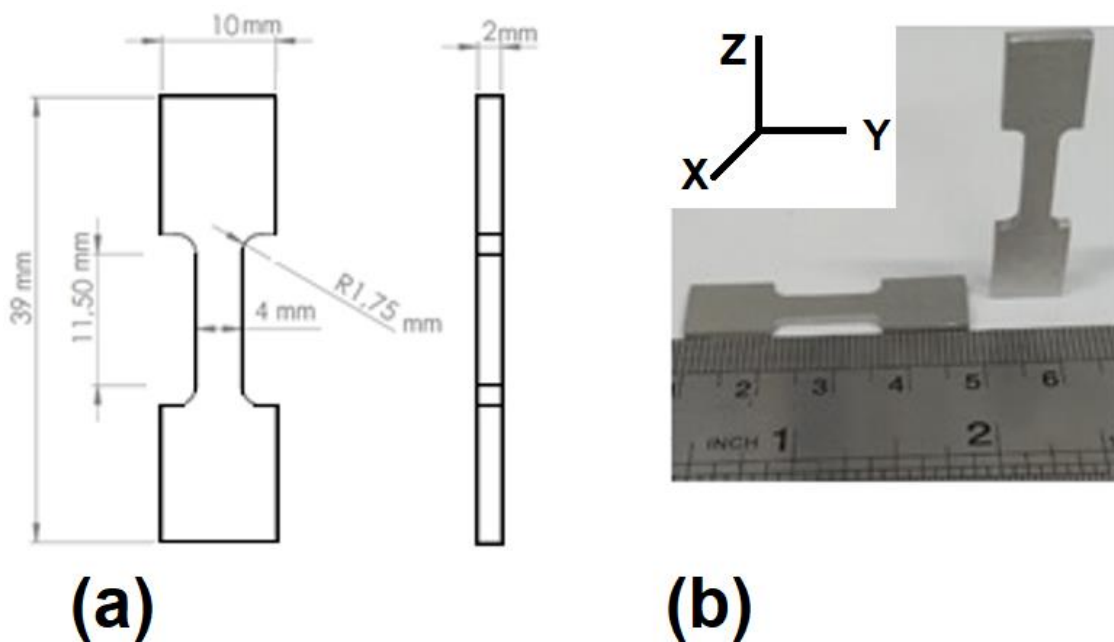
Corpo de Prova para ensaio de tração: (a) corpo de prova com dimensões reduzidas; (b) corpos de prova após usinagem com indicação dos planos em que as barras foram construídas por FSL.
